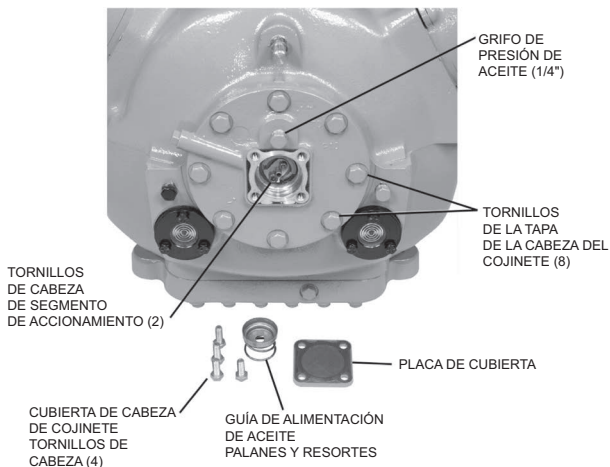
Extracción del cabezal del cojinete del extremo de la bomba (Compresor 06E)
